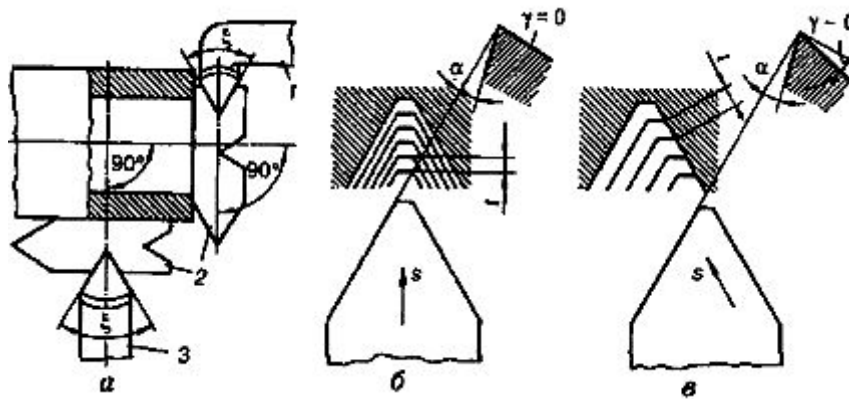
Схеми нарізання різьби різцями на токарному верстаті
